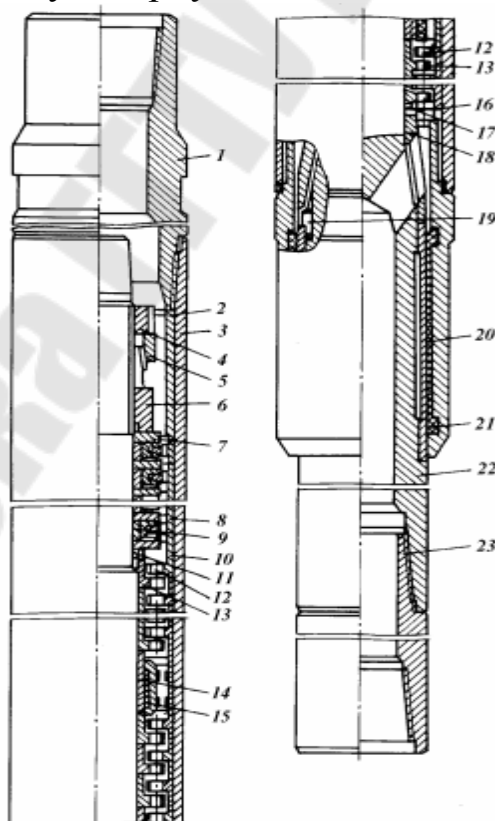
Односекционный турбобур Т12МЗБ-240: 1 – переводник; 2 – втулка корпуса; 3 – корпус; 4 – контргайка; 5 – колпак; 6 – роторная гайка; 7 – диск пяты; 8 – подпятник; 9 – кольцо пяты; 10, 16 – регулировочные кольца; 11, 17 – уплотнительные кольца; 12 – статор; 13 – ротор; 14, 20 втулки средней и
